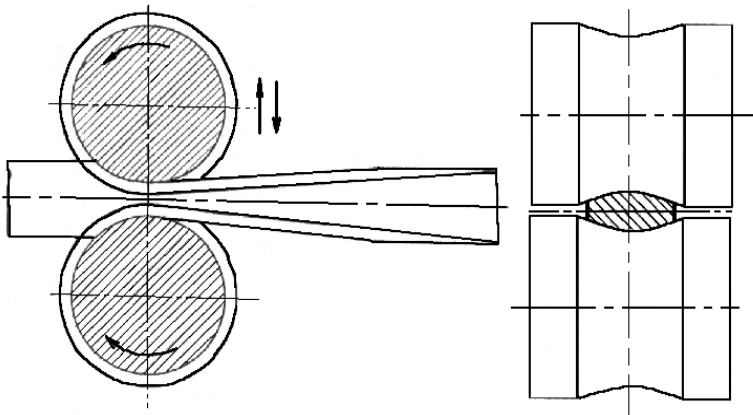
Поздовжньо-копіювальна прокатка заготовок [24]
